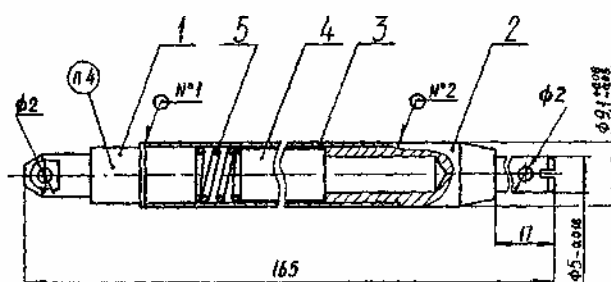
Конструкция модели твэла: 1 – верхняя заглушка; 2 – нижняя заглушка; 3 – оболочка; 4 – стержень из нержавеющей стали; 5 – поджимная пружина. Обозначения мест сварки: №1 – электродуговая сварка; №2 – электронно-лучевая сварка.
